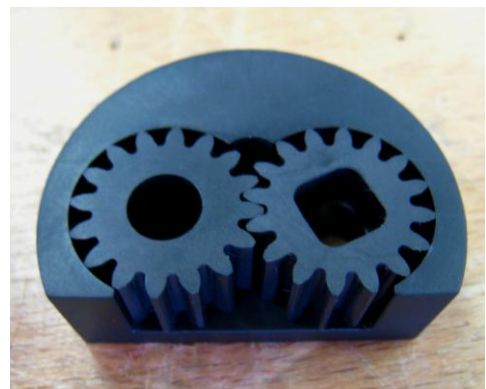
Geöffnetes Gehäuse des 3D-CAD-Modells der Prototypenpumpe
